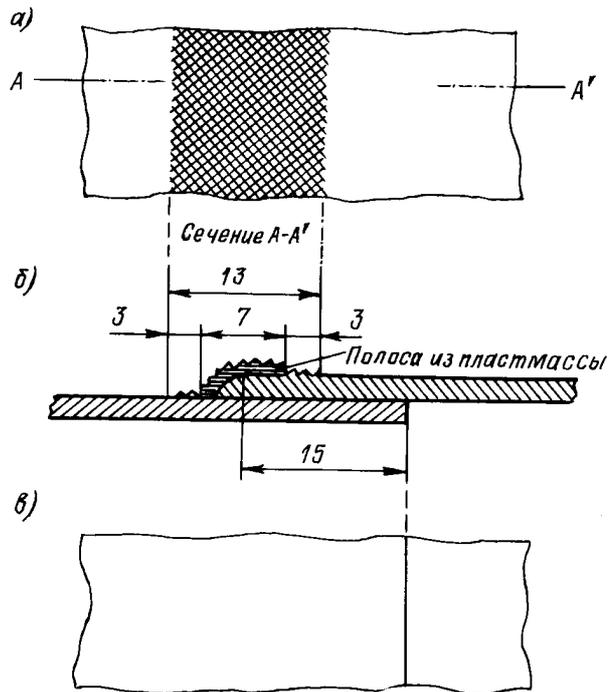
Чехол, изготовленный из нескольких кусков ткани, соединенных пайкой (размеры показаны в мм):
